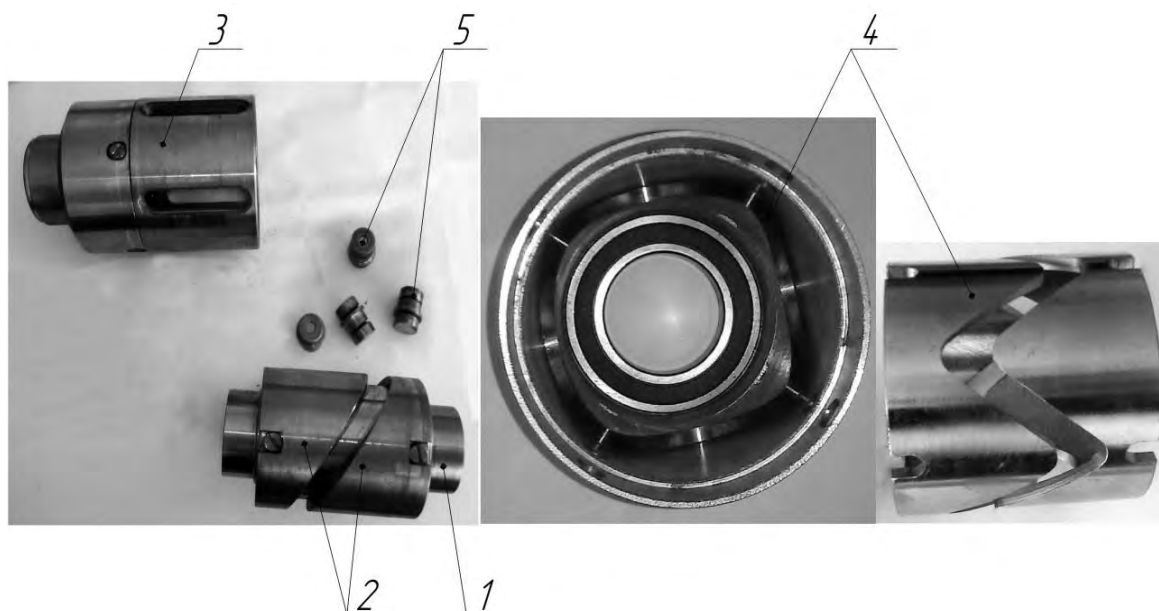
Опытный образец передачи (а) и редуцирующий узел (б)
